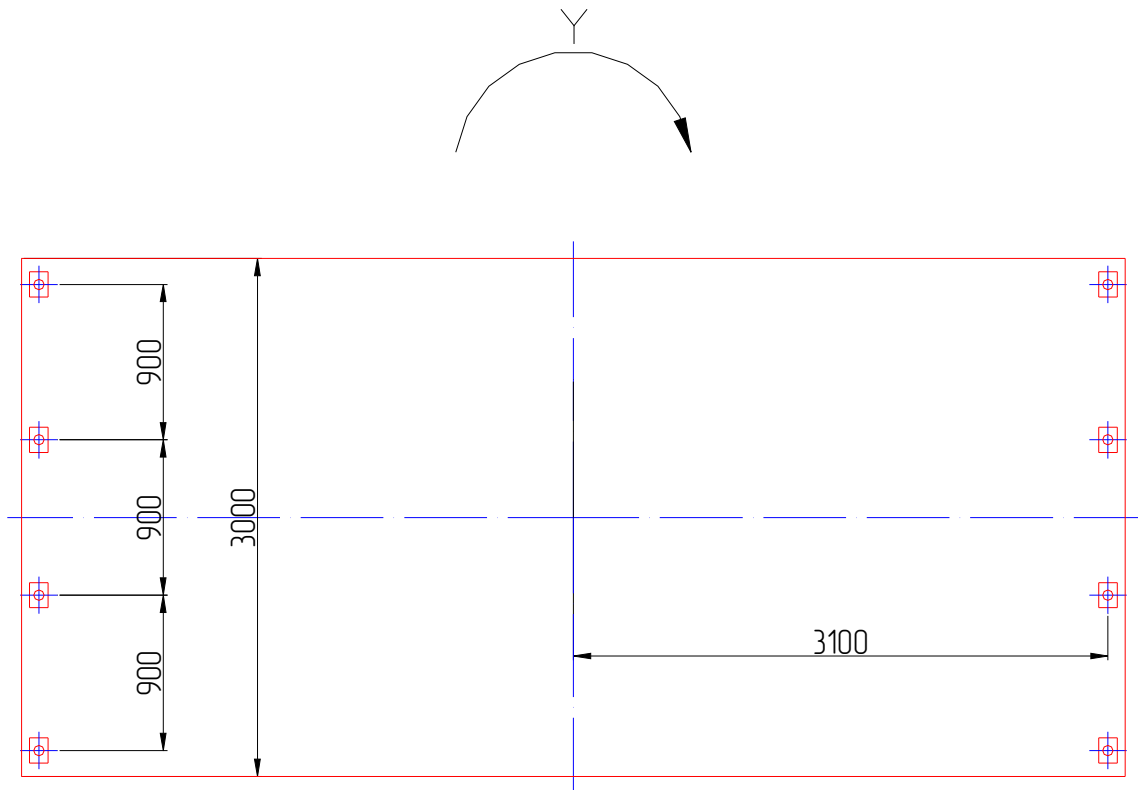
Схема кріплення рами пили гарячого різання до фундаменту
